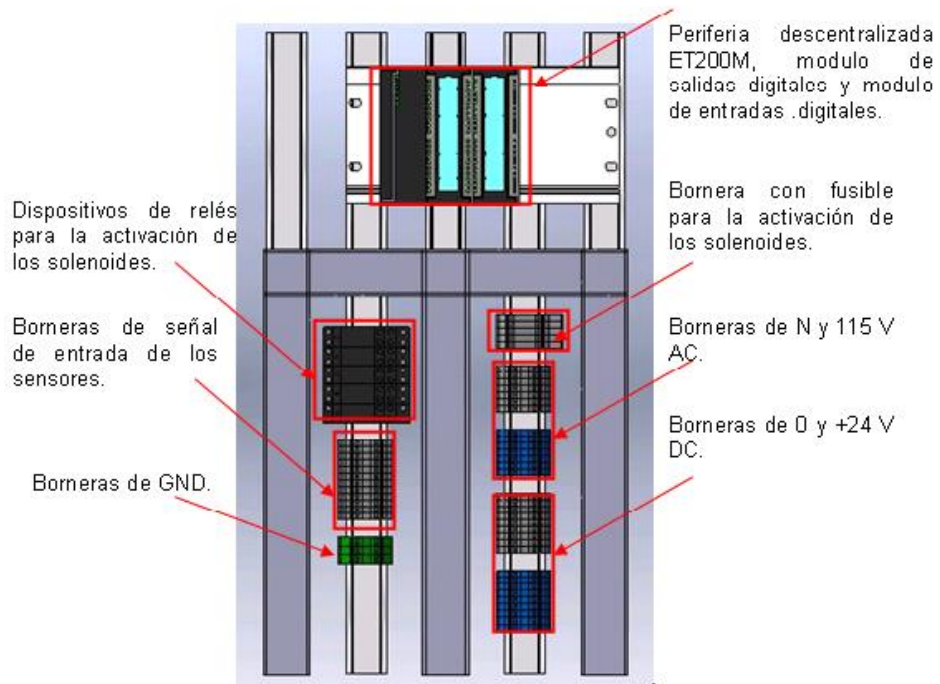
Dispositivos del tablero ubicado en la segunda estación
